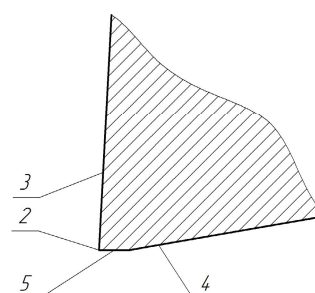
Усовершенствованная конструкция шевера с винтовыми режущими кромками (вид Б)
